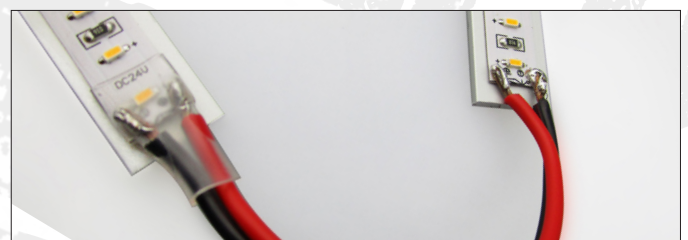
Isolierung der Lötstellen: idealerweise mit einem Schrumpfschlauch
